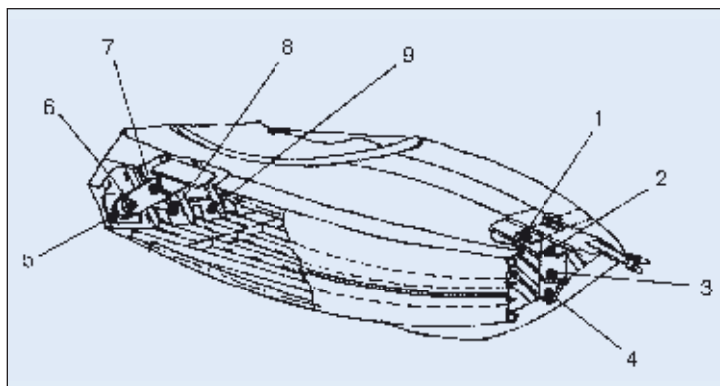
Электродинамическая обработка сварных соединений стоек подкрепления корпуса
